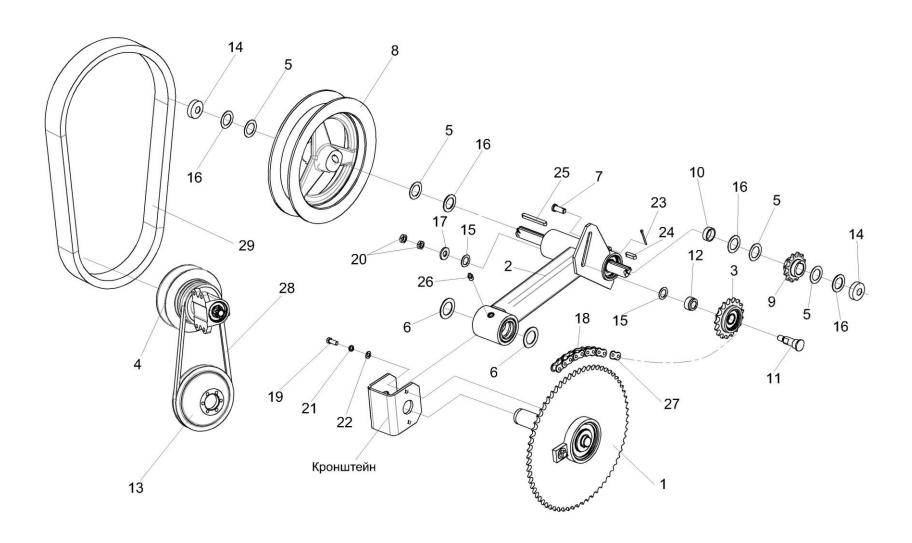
Установка привода вариатора КЗР 1514100А
